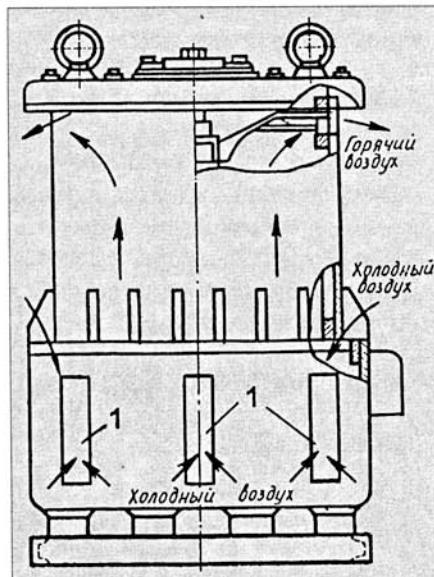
Общий вид преобразователя ВПЧ-100-2400 с вырезами для дополнительного охлаждения (1 — вырезы в обшивке преобразователя)
